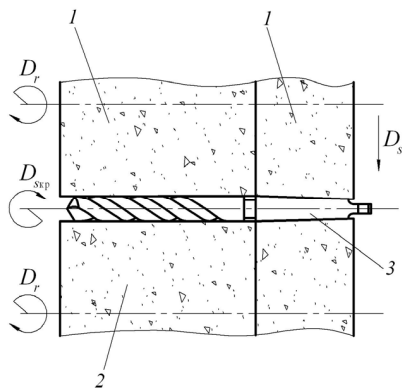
Совмещенное бесцентровое шлифование заготовки сверла: 1 – рабочие круги; 2 – ведущий круг; 3 – заготовка
